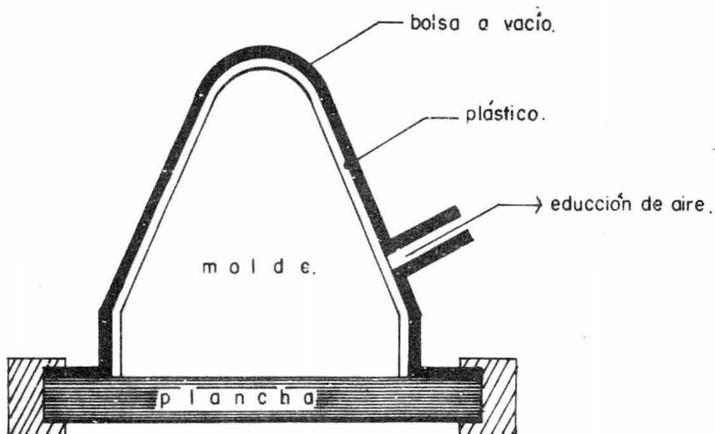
REFORZADO.- MOLDEO EN BOLSA AL VACIO.
